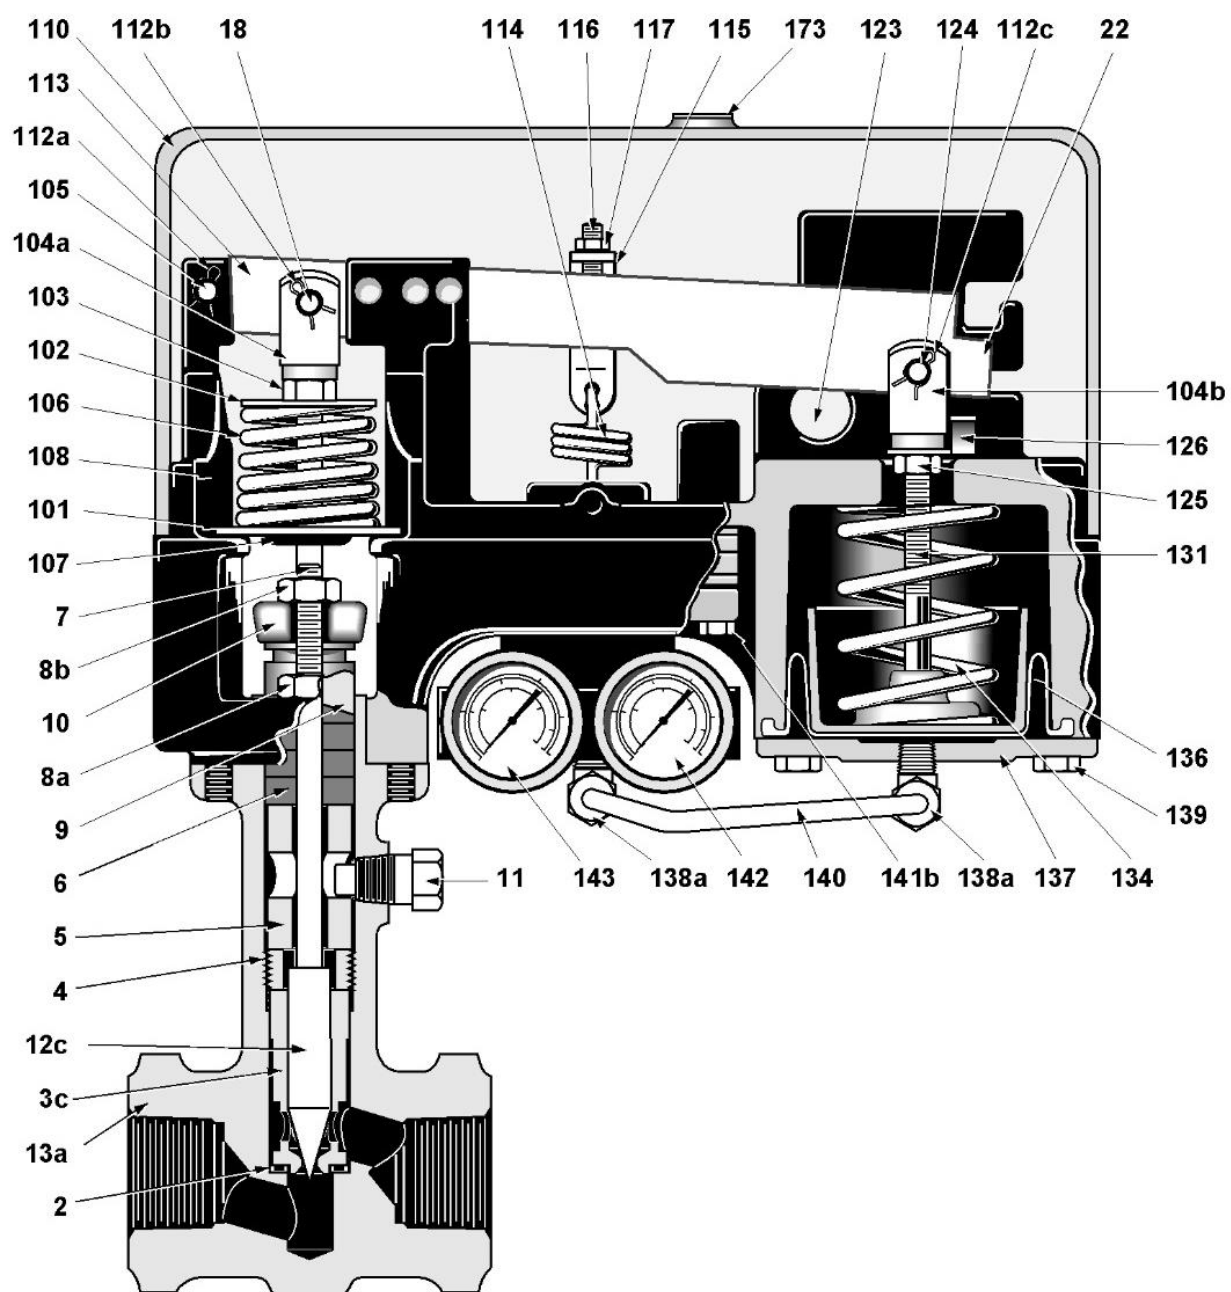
Клапан «ВАРИПАК» 28001 с одним рычагом и пневматическим исполнительным механизмом обратного действия «Воздух открывает»
